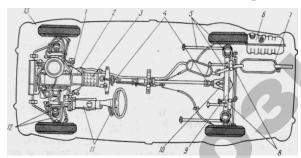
Общая компоновка заднеприводного автомобиля BA3-2105 с передним продольным расположением двигателя:
